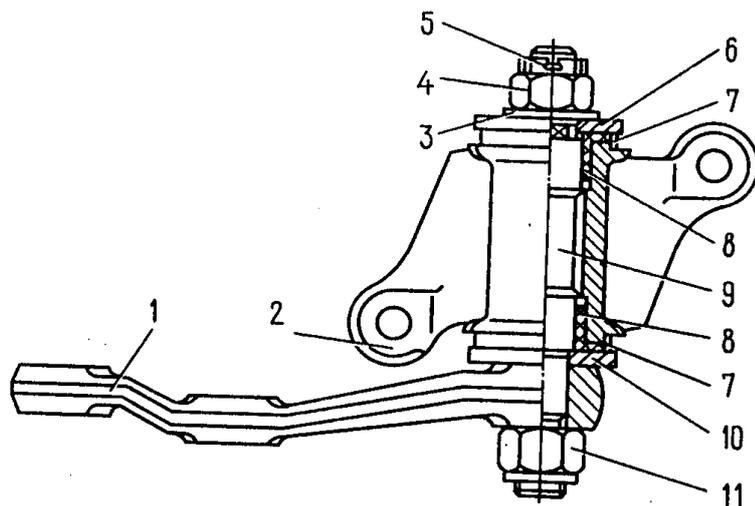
Corte del soporte de la palanca pendular: 1. - palanca pendular; 2- cuerpo del soporte; 3 arandela; 4- tuerca de regulación; 5 - clavija de aletas; 6- arandela superior; 7- empaquetadura; 8- casquillo; 9- eje de la palanca; 10 arandela inferior; 11 - tuerca de autofrenado
